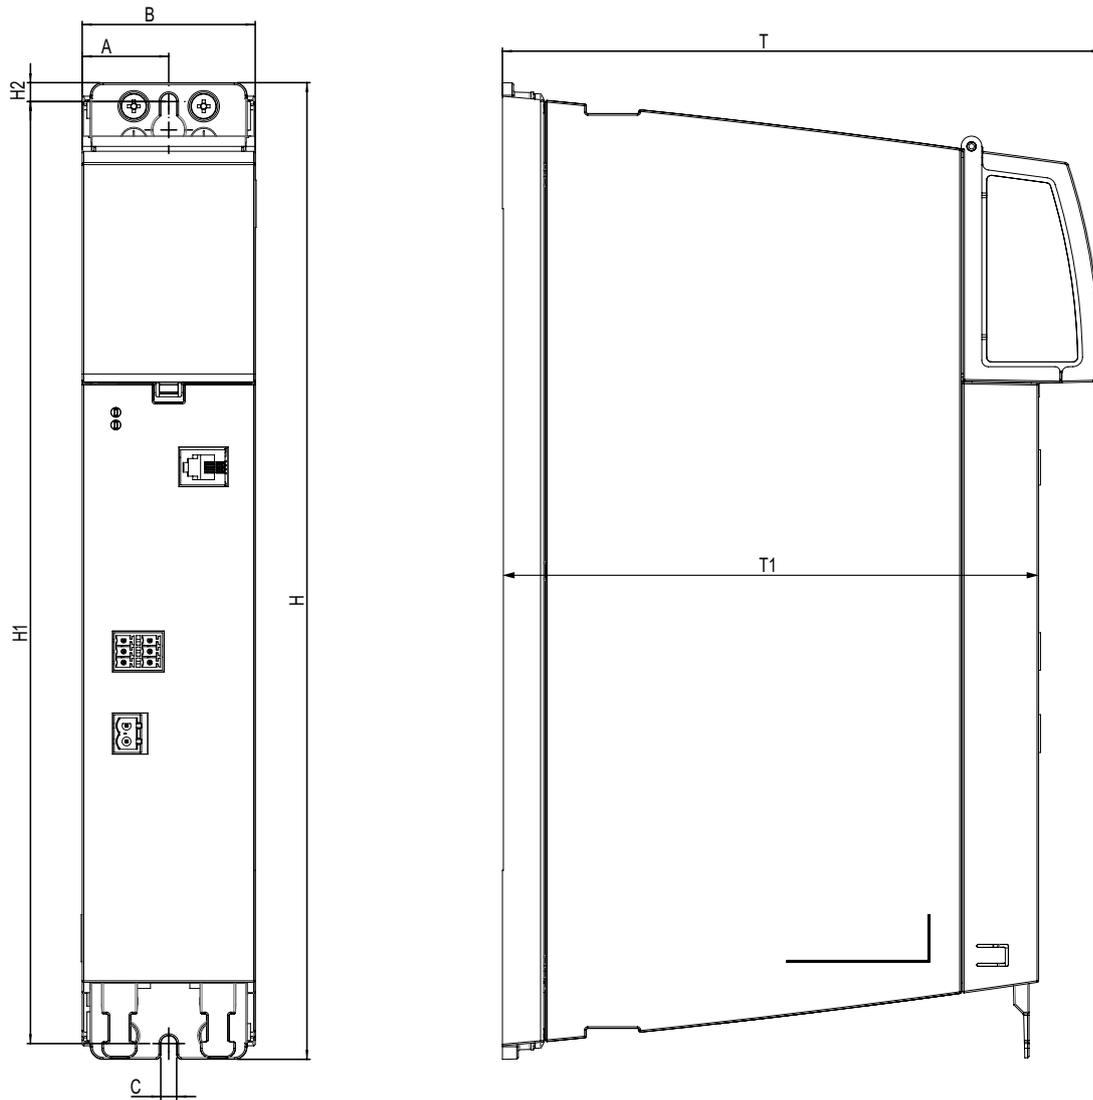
JM-3000 电源装置 BG1 冷却板尺寸图（尺寸请参见表 2.2）
